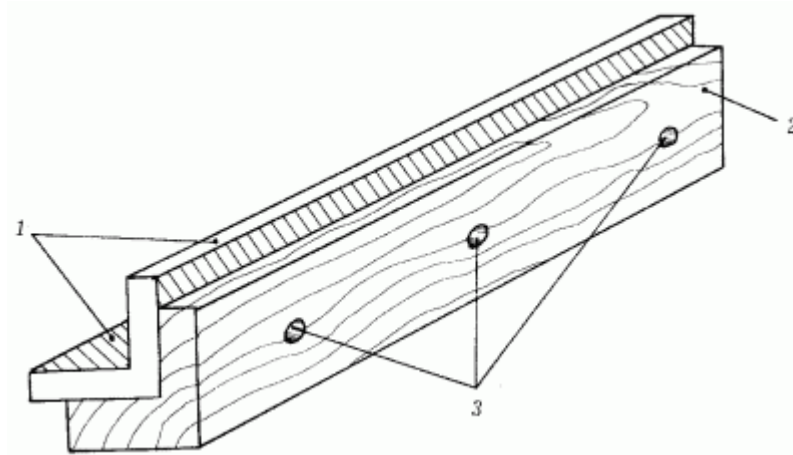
Приспособление для опилования кромок деталей из листового металла:
